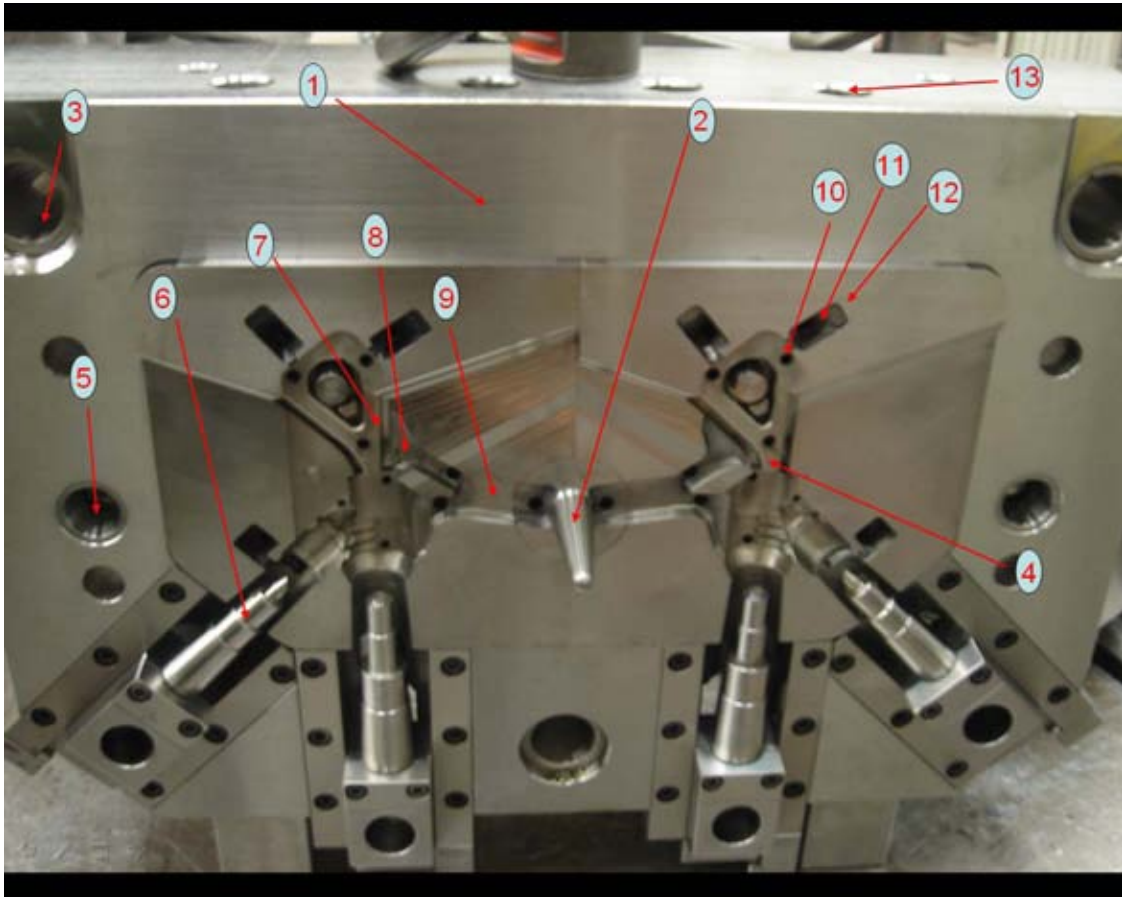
Muestra las partes del molde de la cavidad móvil [2].
